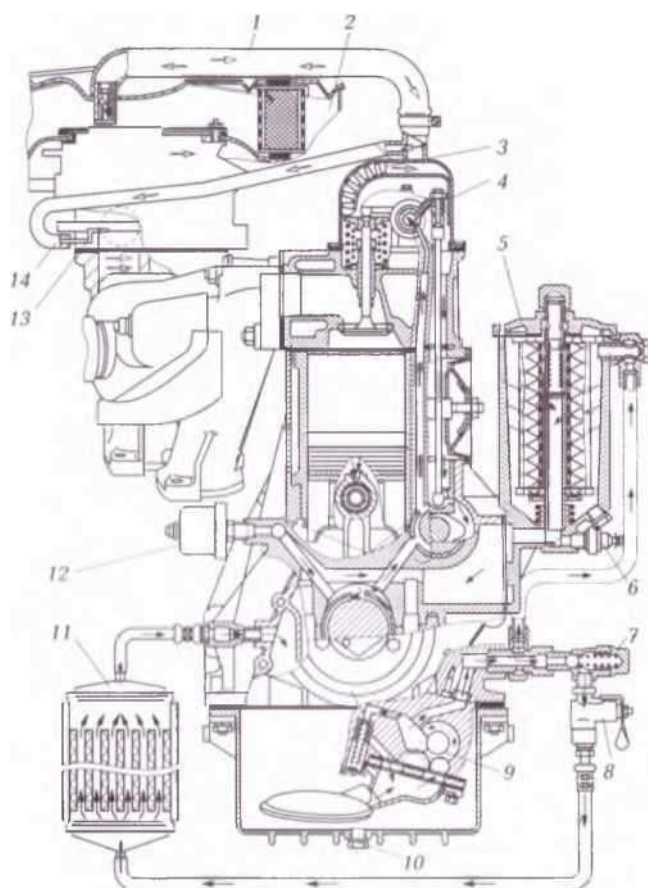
Смазочная система и система вентиляции картера двигателя автомобиля ГАЗ-31029:
